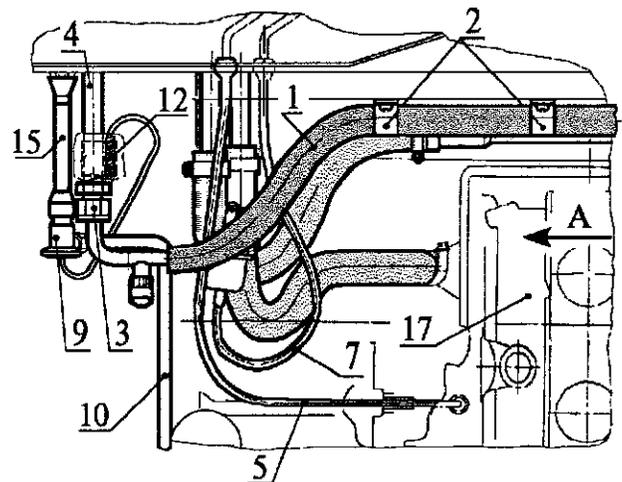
Отсоединение трубопроводов от блока обработки воздуха:
